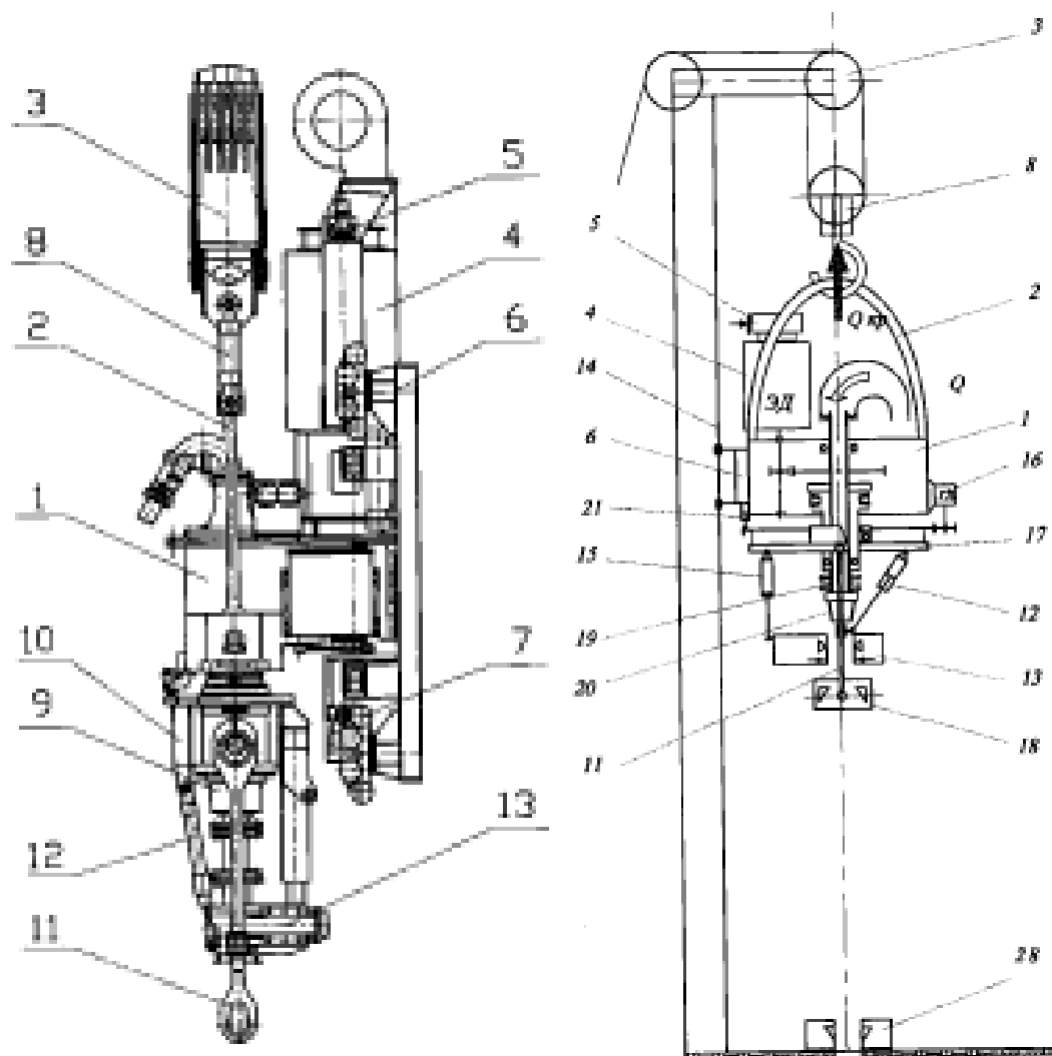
Схема верхнего привода: 1 – вертлюг-редуктор; 2 – штропы вертлюга-редуктора; 3 – талевая система; 4 – электродвигатель постоянного тока; 5 – диско-колодочный тормоз; 6 – рама с роликами (каретка); 7 – блок роликов; 8 – система разгрузки резьбы; 9 – трубный манипулятор; 10 – вертлюжная головка; 11 – штропы элеватора; 12 – гидроцилиндры отвода штропов элеватора; 13 – трубный зажим; 14 – направляющие мачты; 15 – гидроцилиндр управления трубным зажимом; 16 – гидродвигатель; 17 – траверса вертлюжной головки; 18 – элеватор; 19 – шаровой кран; 20 – ниппель; 21 – стопорное устройство; 28 – клиновой захват.
